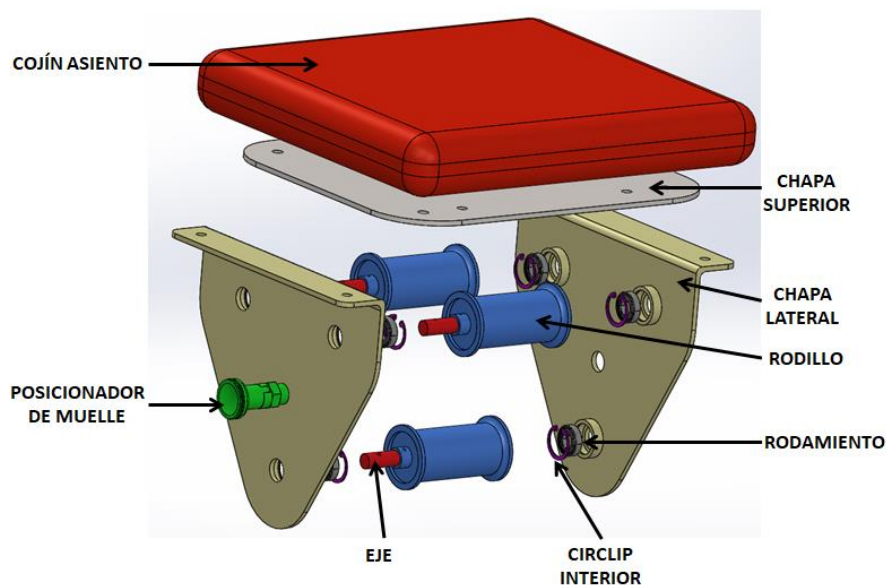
Vista explosionada de las piezas que componen el asiento móvil.
